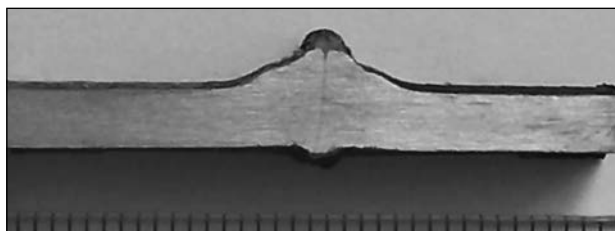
Макрошліф зварного з'єднання труби діаметром 51 × 3,5 мм
